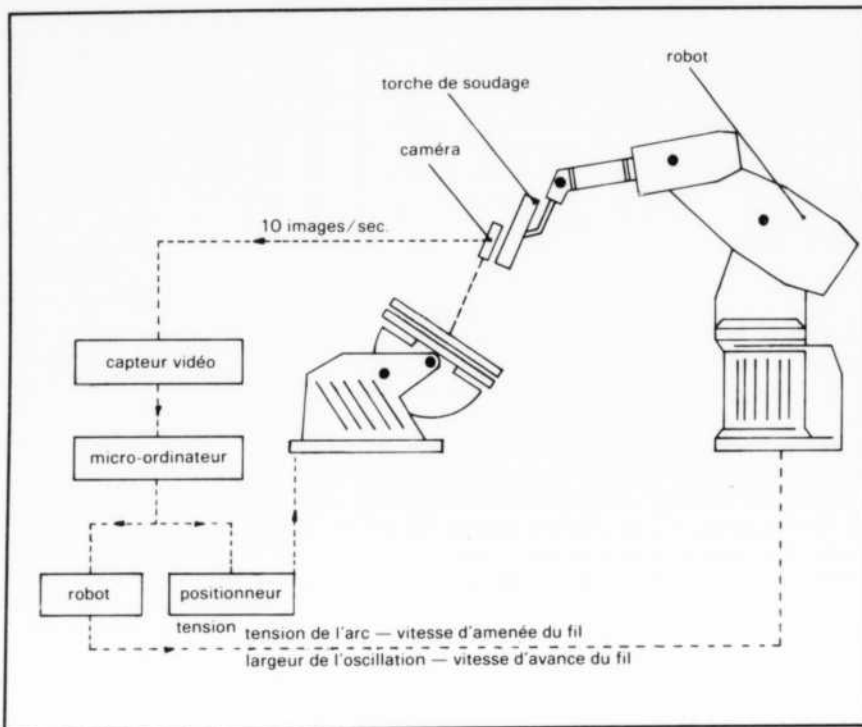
Composante d'un procédé de soudage automatisé
